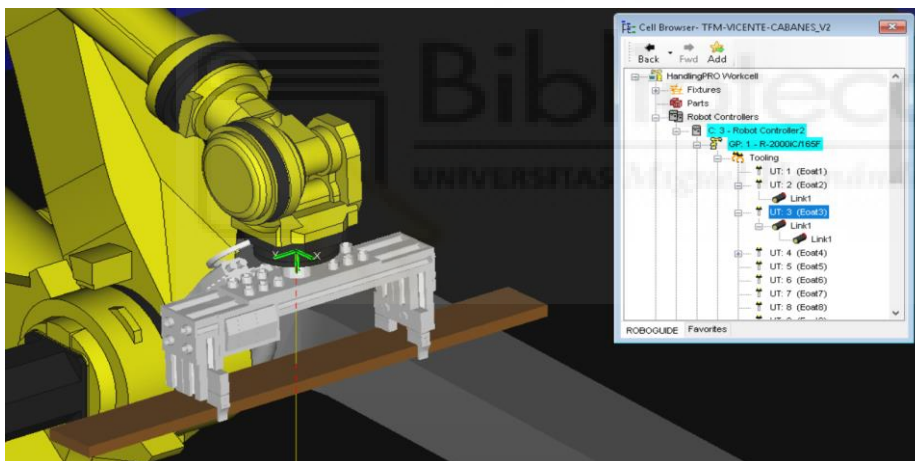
a 56 Diferentes herramientas robot 01 Roboguide
